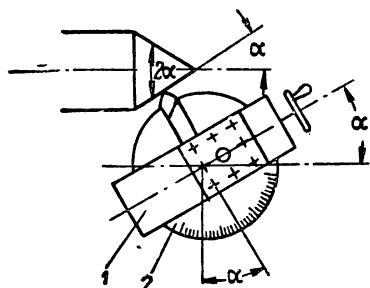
Схема обработки наружной конической поверхности при повернутых верхних салазках суппорта.
